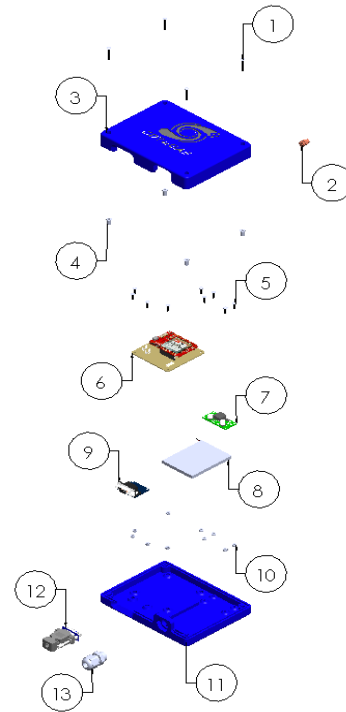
Explosionado case electrónica ICU. Fuente: Autor
